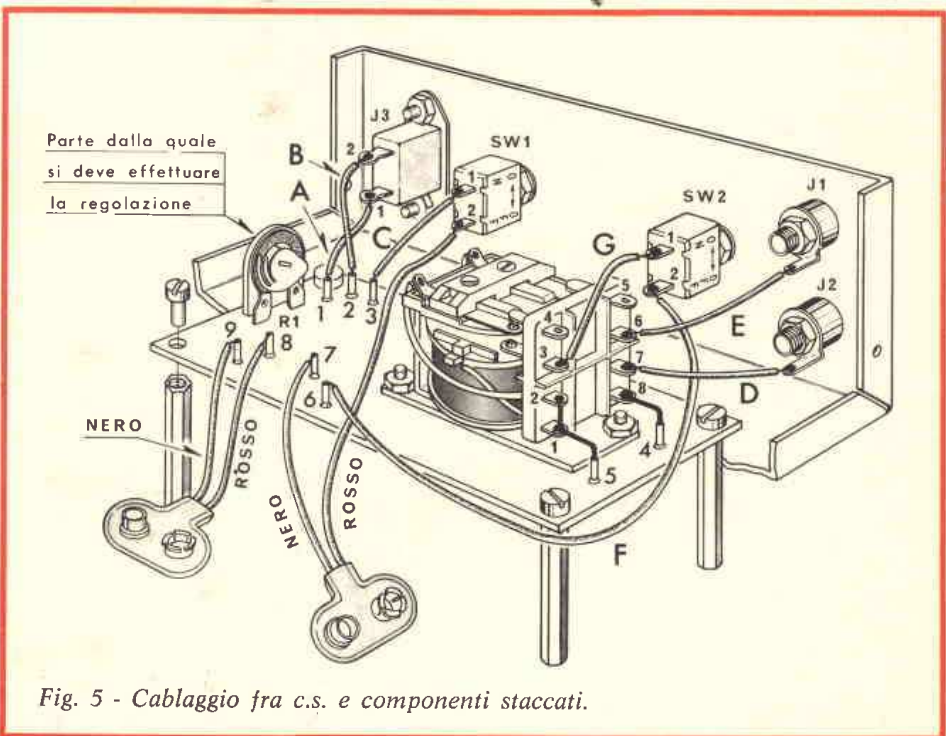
Cablaggio fra c.s. e componenti staccati.
